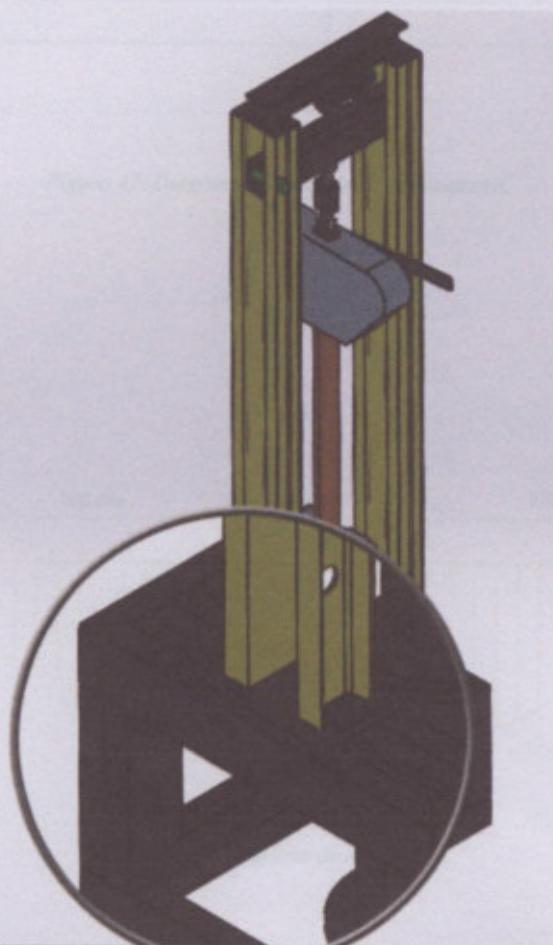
Vista isométrica de la maquina con zoom en los UPN horizontal a dimensionar.
